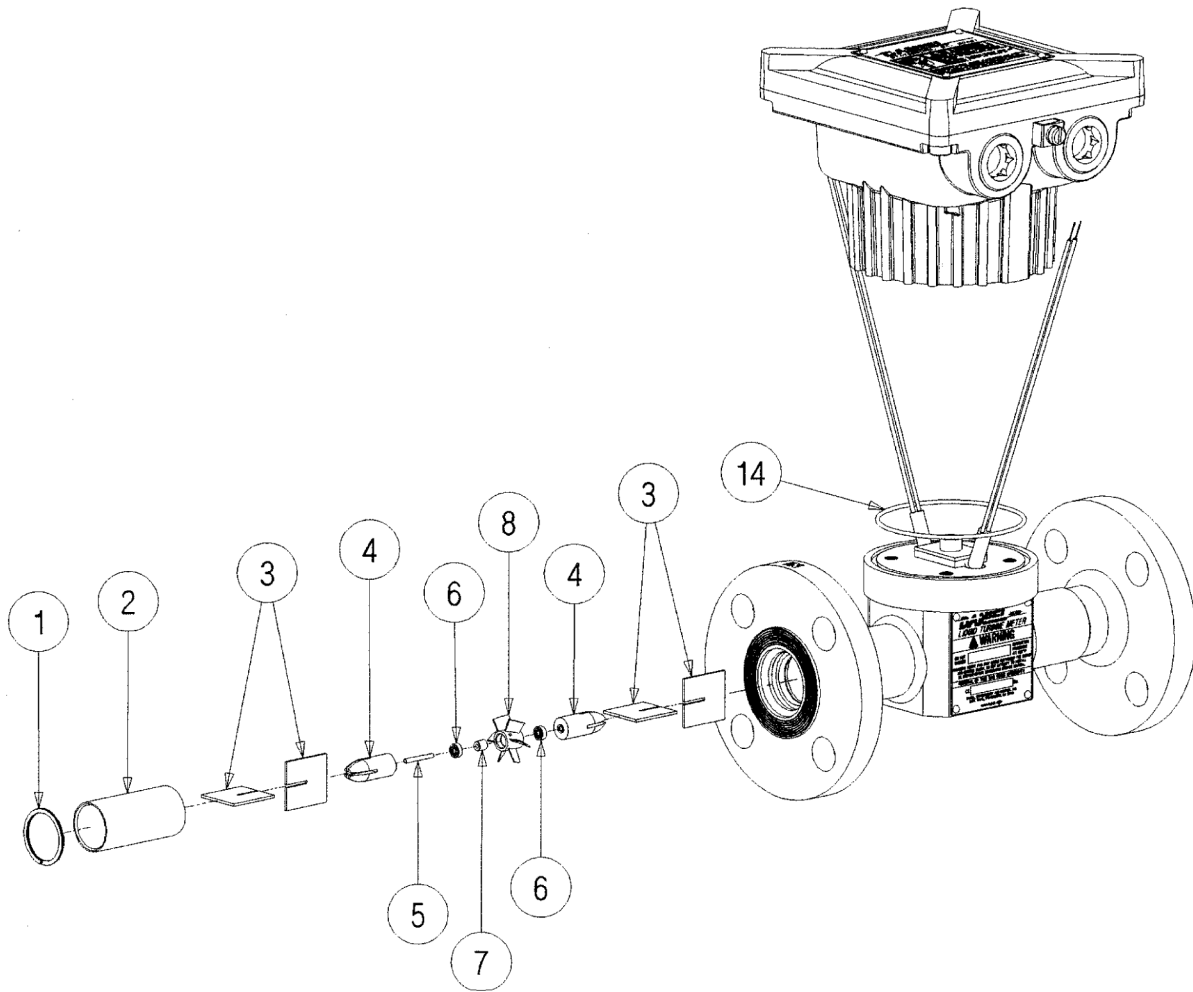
Conjunto do Medidor (1") - Rolamentos Internos de Aço Inoxidável
